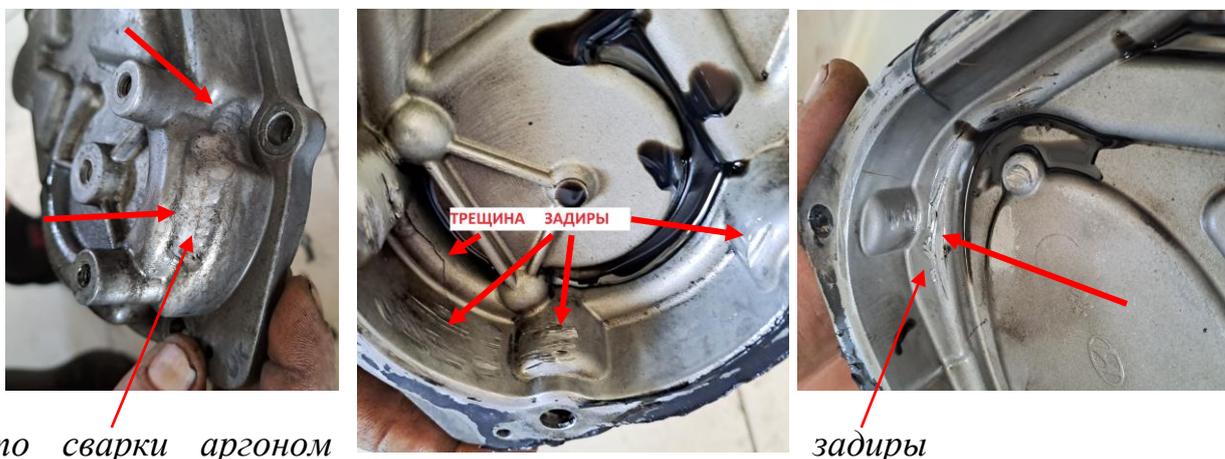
Кожухи (крышки) цепи С (выдержка из ТИС [3.6]).
